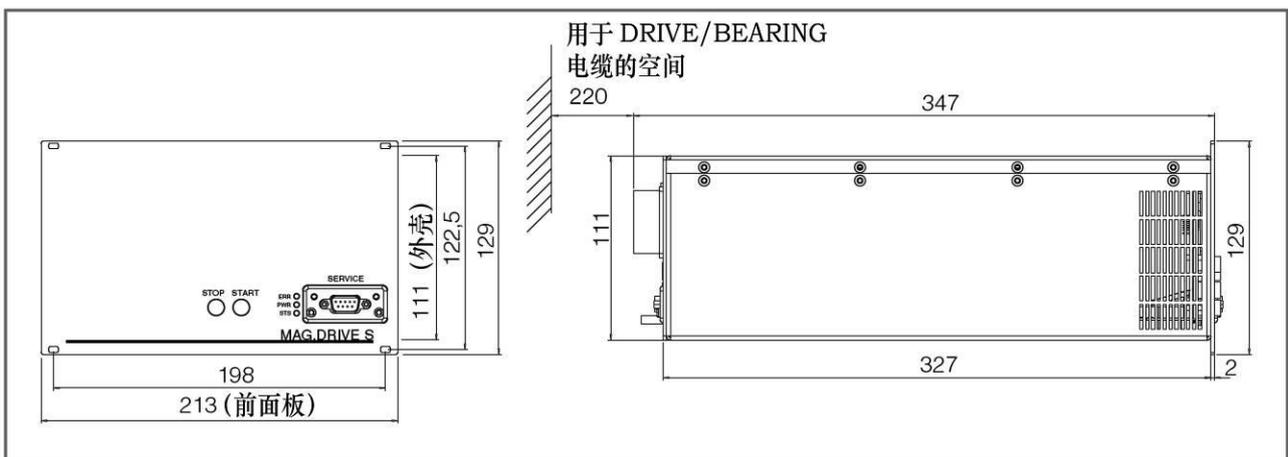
MAG.DRIVE S 的尺寸图，尺寸单位为 mm
